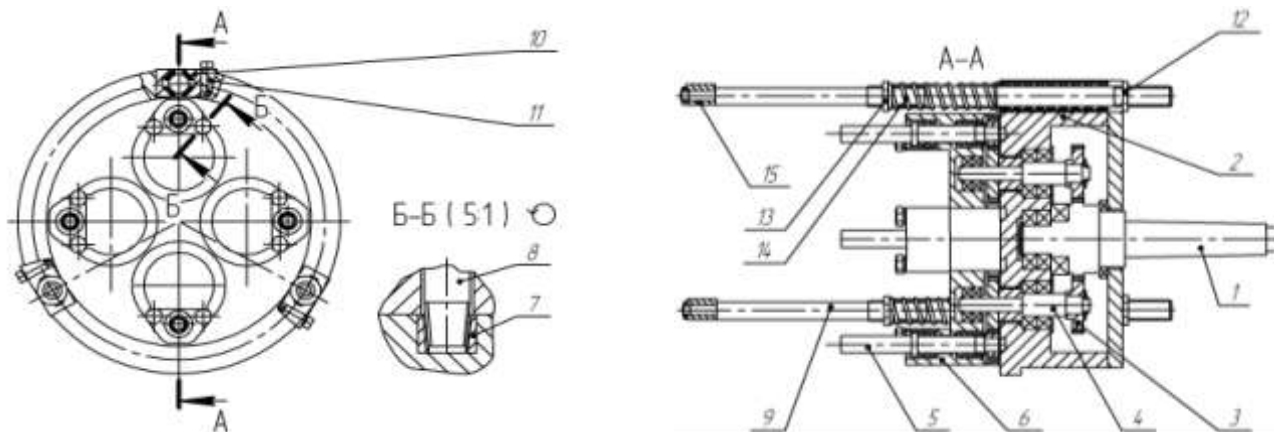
Багатошпindelна головка для токарного верстата (пат. України № 36305): 1 - вал-шестірня; 2 – корпус; 3 – шестірня; 4 – вал; 5 – шпindel; 6 – корпус шпindelю; 7 – розрізна вставка; 8 – болт; 9 – пересувна скалка; 10 - напрямні кочення; 11 – затискний клин; 12, 13 – гайка; 14 – пружина; 15 - ексцентрикова втулка
